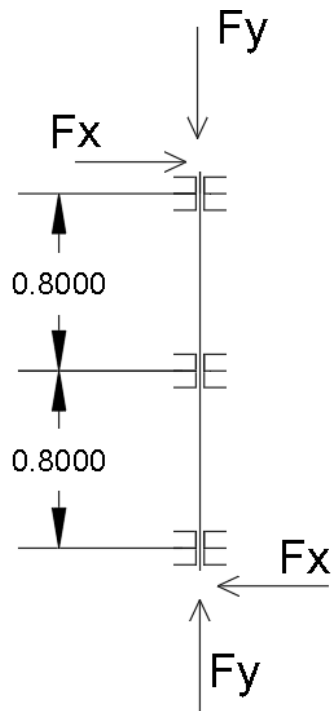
Diagrama fuerzas aplicadas a la varilla deslizante
